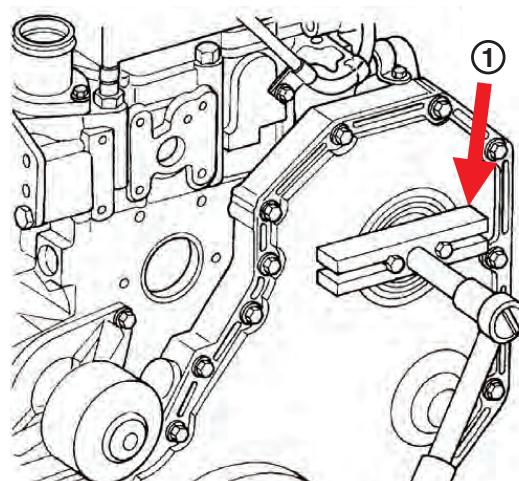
Separar el mecanismo de la bomba de inyección del eje de la bomba
